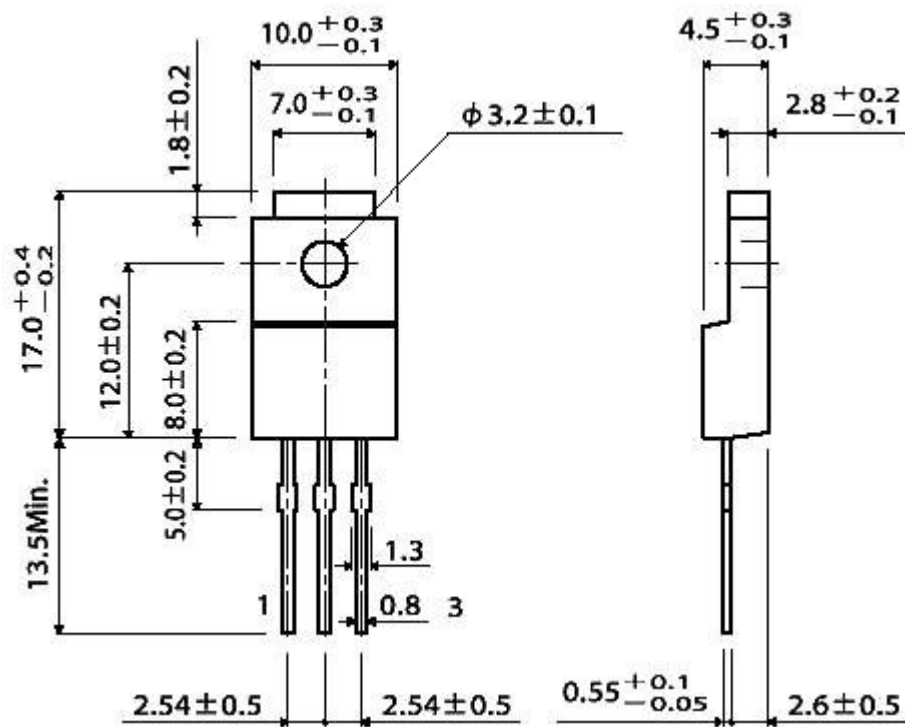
Габаритні розміри стабілізатора L7805
